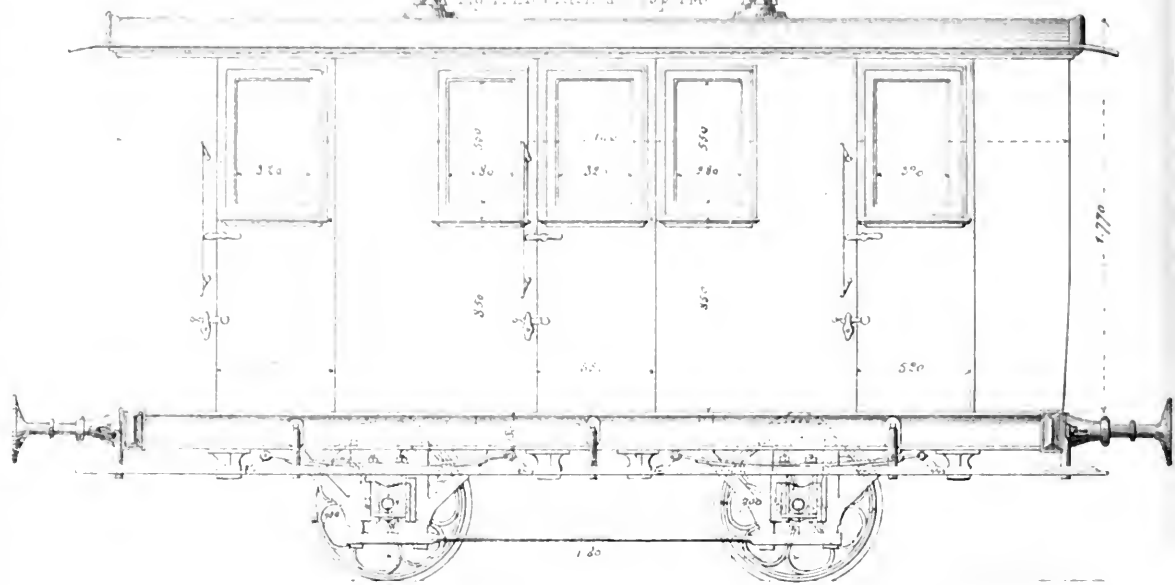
Plan, Marches et Coupes de la Chaise à 0^m03 pour 1 M^e
